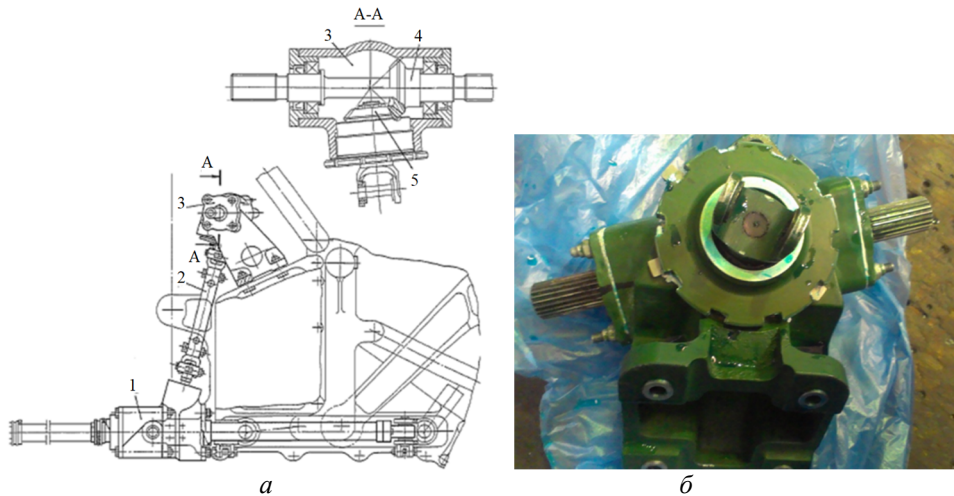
Установка підйомника №1 на нервюрі крила №6: а – конструктивна схема та розташування кінцевого редуктора, б – фото кінцевого редуктора.
